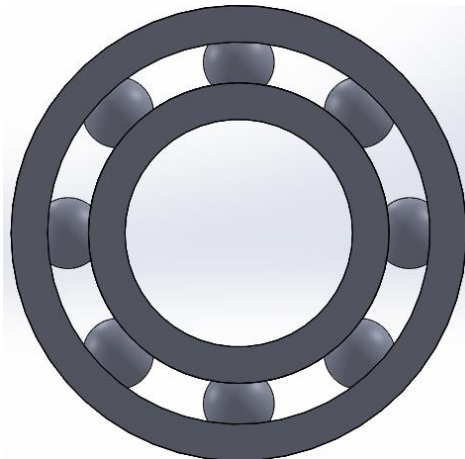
Dibujo explosionado del rodamiento o balero. Diseñada con SolidWorks®.
